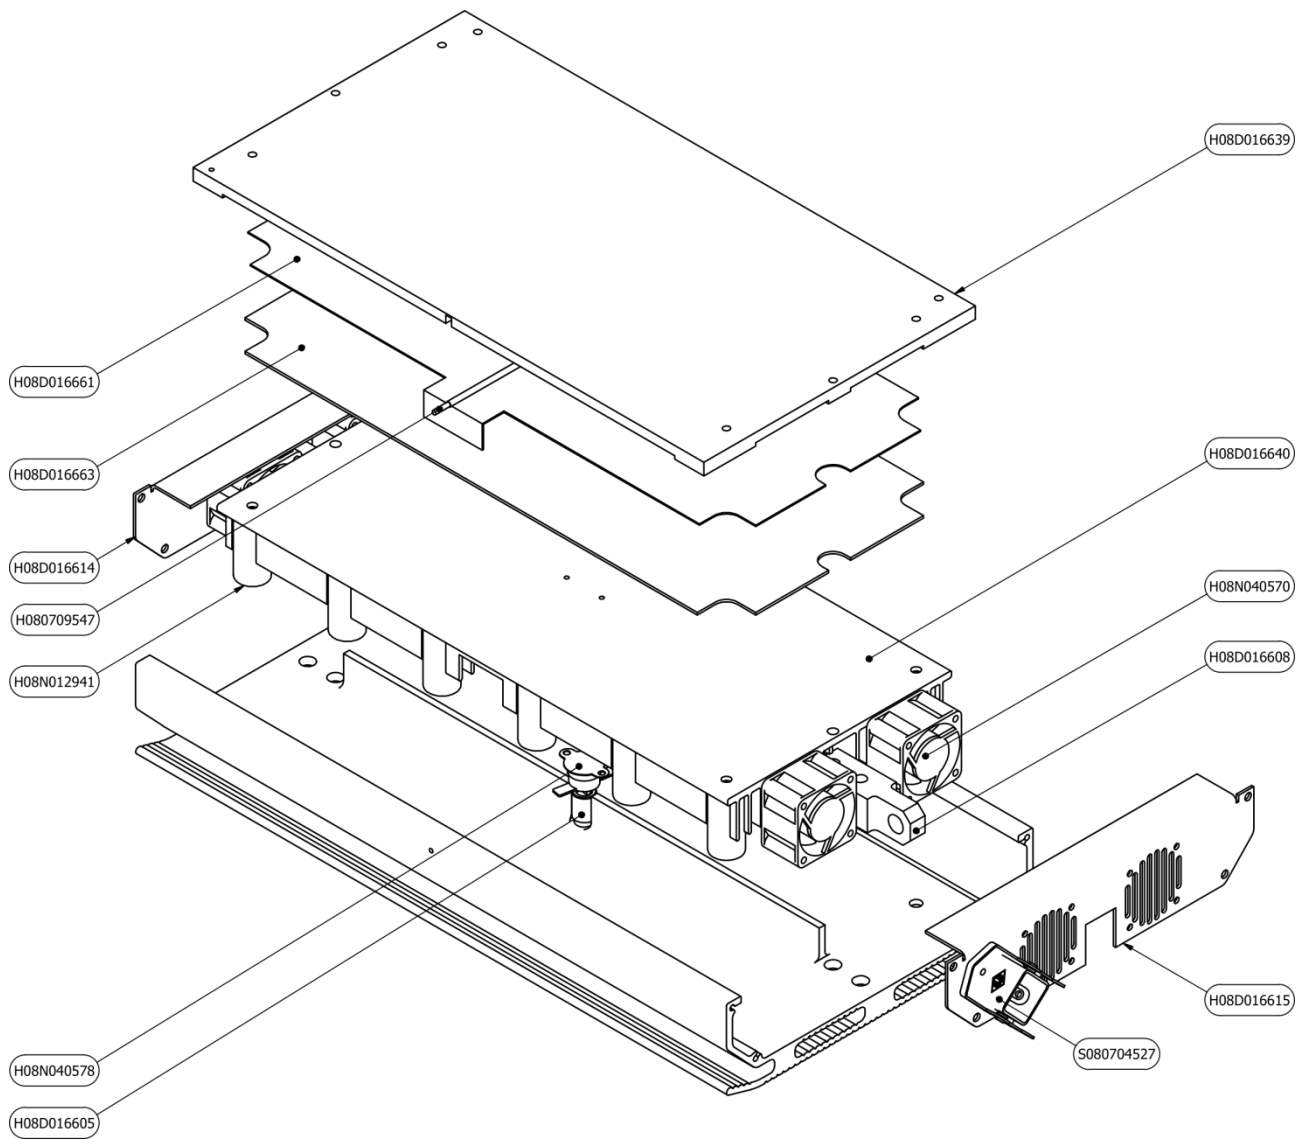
H08D016641 Assemblage de la plaque chauffante inférieure PML-300
